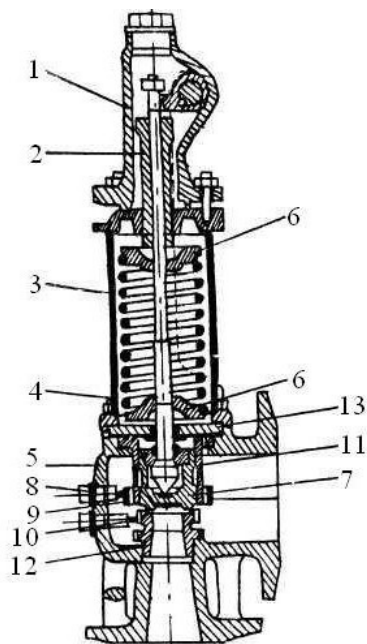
Клапан предохранительный пружинный типа СППК4Р (до 450 °С): 1 – колпак; 2 – регулировочный винт; 3 – крышка; 4 – шпилька; 5 – корпус; 6 – опорные шайбы; 7 – золотник; 8 – стопорные винты; 9 – регулировочная втулка верхняя; 10 – регулировочная втулка нижняя; 11 – направляющая втулка; 12 – сопло; 13 – перегородка
